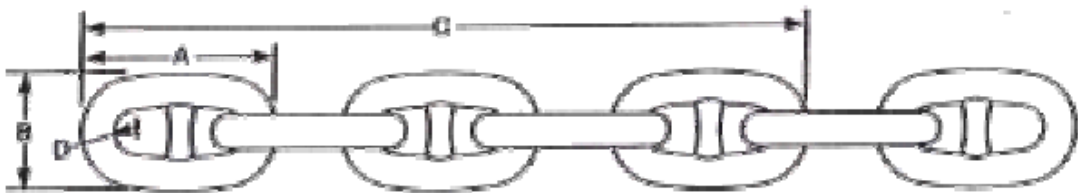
Perfil de la cadena compuesta de acero. Fuente: .<sup>1</sup>
